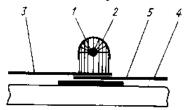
Схема сварки ИК-излучением:
